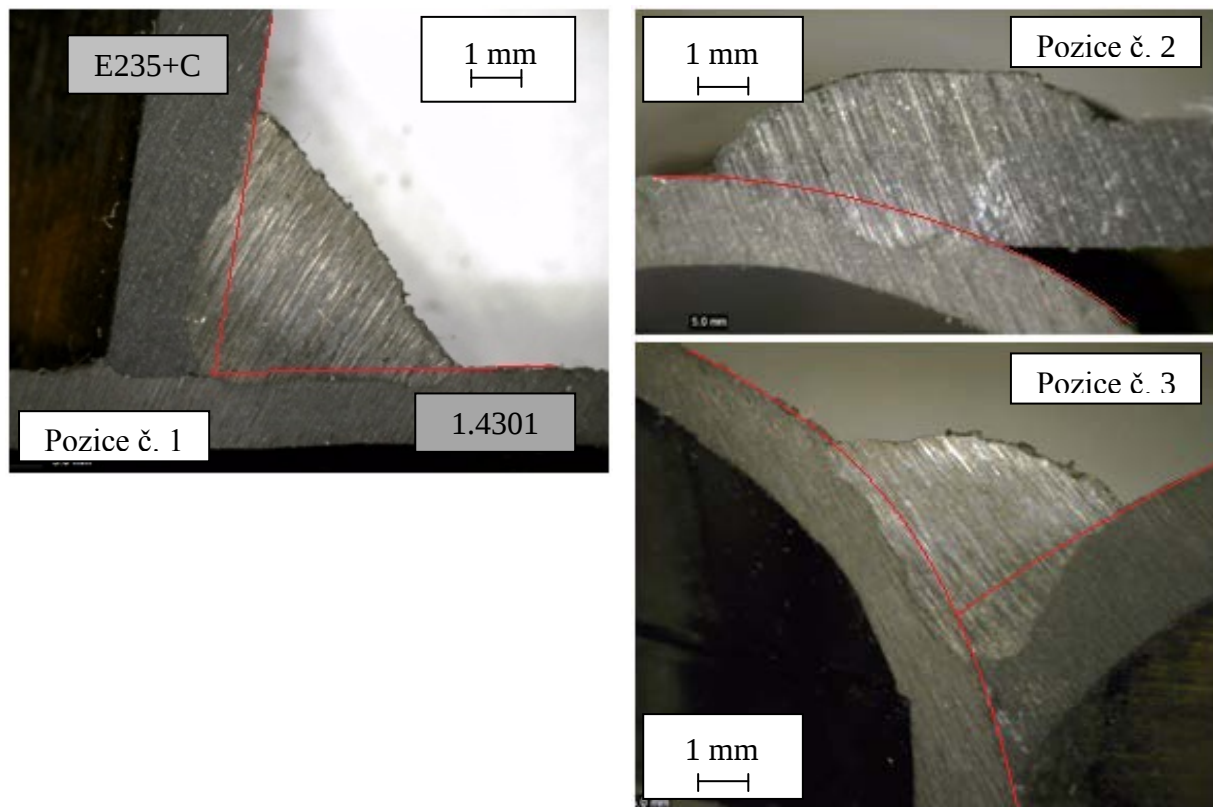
Makrostruktura svaru G8 vzorku č. 1
